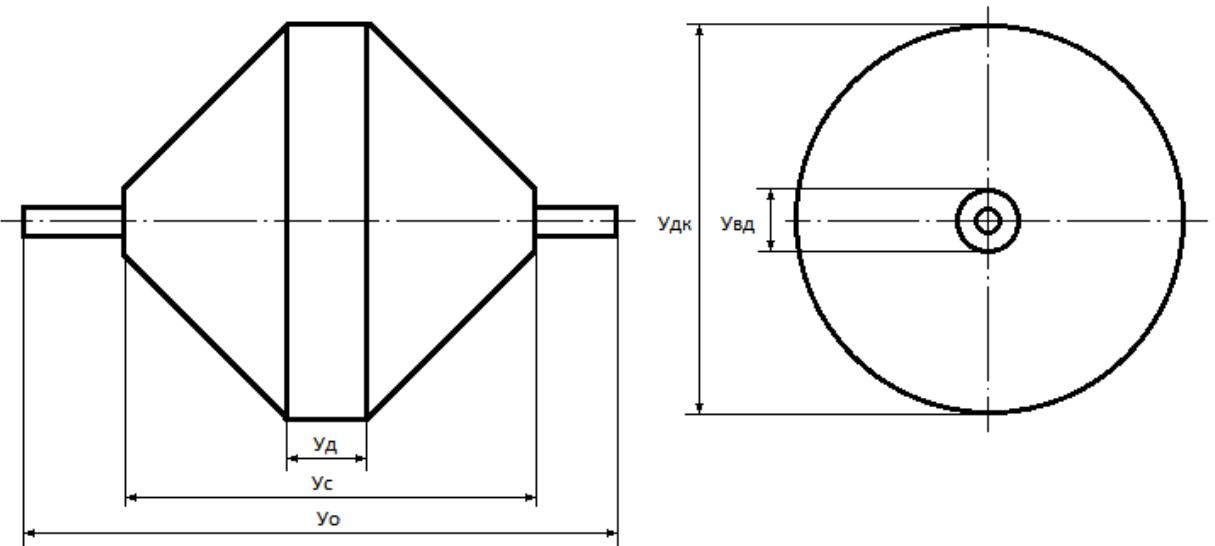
Основные конструктивные размеры уплотнителя стен и дна арыка
